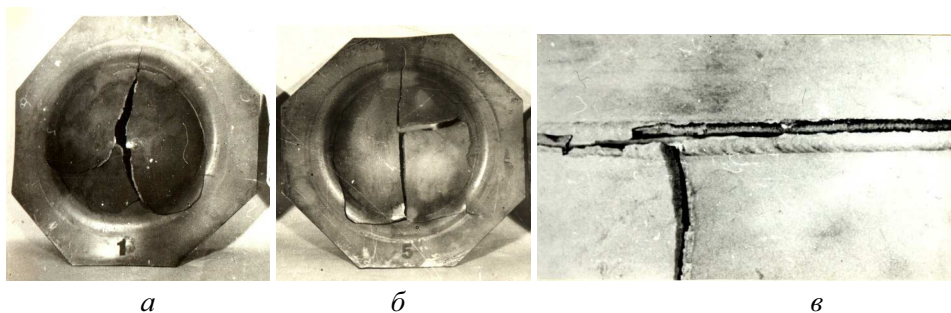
Характер разрушения пластин при двухосном нагружении: *а* – основной металл; *б* – сварные пластины; *в* – линия разрушения сварного соединения
